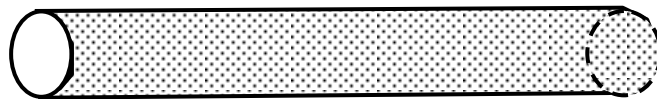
Трубчатая цилиндрическая заготовка для первичного роздува
